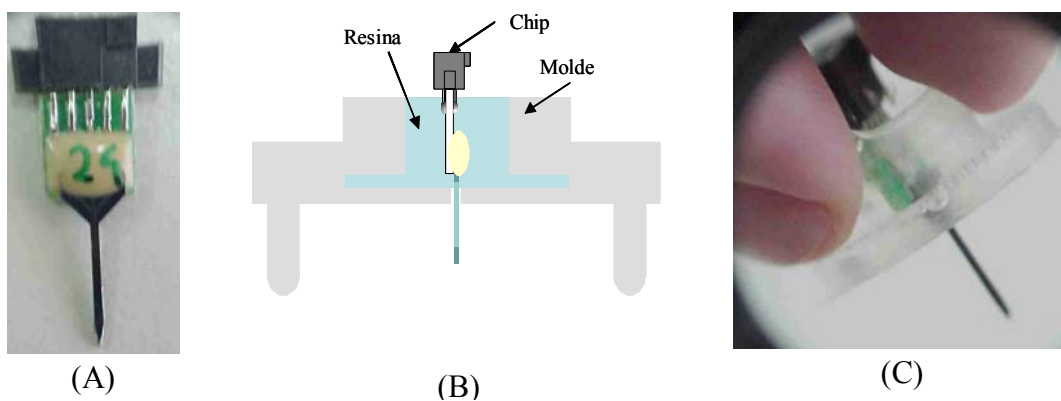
Proceso de encapsulación del chip: (A) chip montado sobre la placa PCB, (B) Estructura del molde y (C) fotografía del chip encapsulado.
